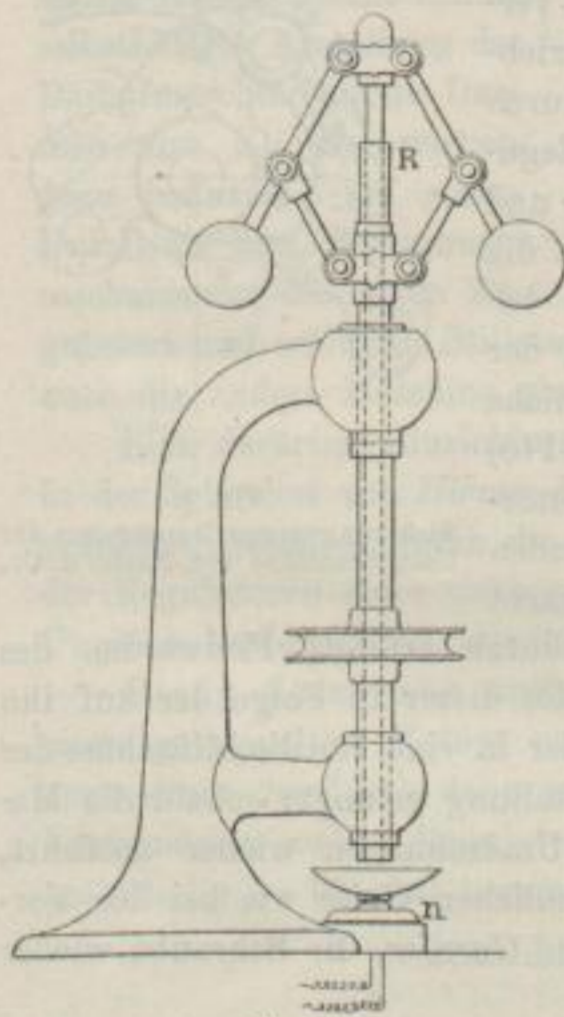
Regulator mit Sicherung gegen Durchgehen der Maschine.
